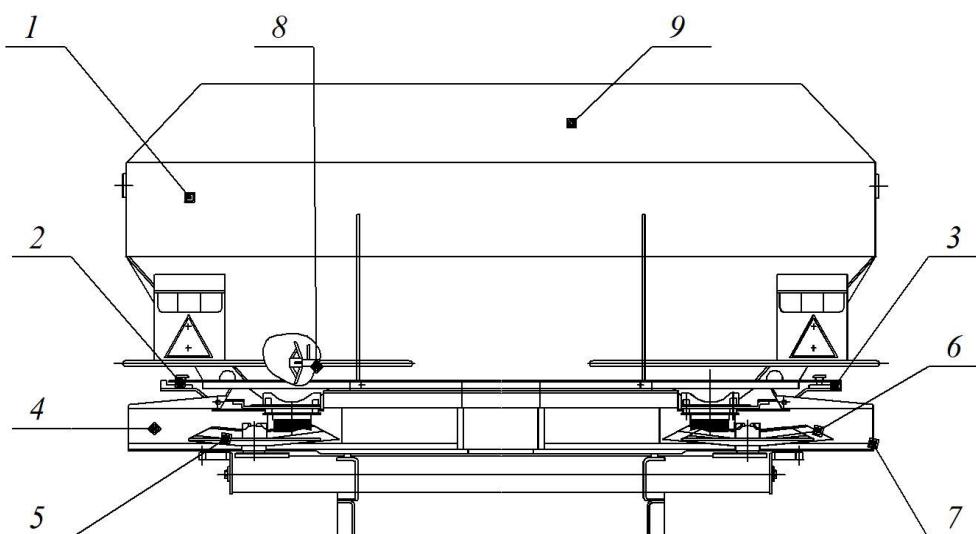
Общий вид рассеивателя РУ-1600: 1 – бункер с рамой; 2 – механизм дозирующий правый; 3 – механизм дозирующий левый; 4 – отражатель правый; 5 – метатель (рассеивающий диск) правый; 6 – метатель (рассеивающий диск) левый; 7 – отражатель левый; 8 – рыхлитель (сводоразрушитель); 9 – тент
